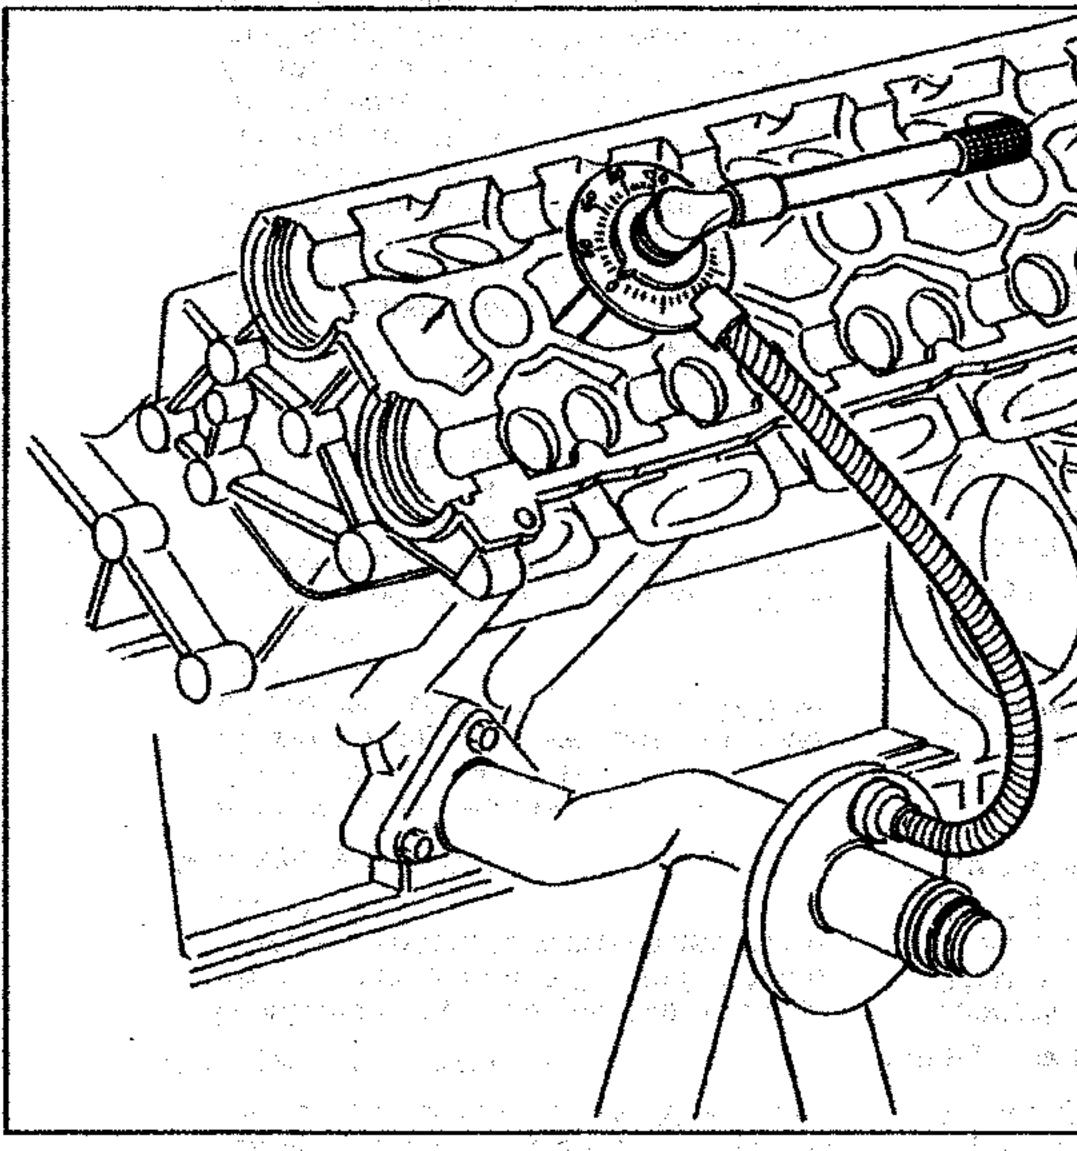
= Serraggio teste con atrezzo Fig. 40 = Fitting heads with USAG 830 tool Fig. 40 = Serrage des culasses avec outil USAG 830 Bild 40 = Anziehen der Zylinderköpfe mit USAG 830 Werkzeug USAG 830 • •
